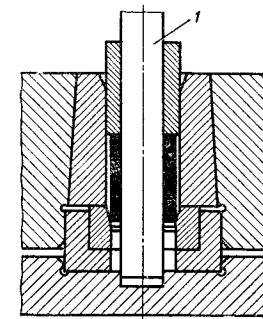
Схема наладки инструмента для прямого выдавливания полых заготовок с нижним центрированием оправки
